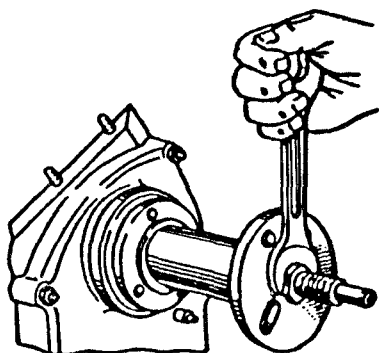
Напрессовка ступицы шкива коленчатого вала с помощью приспособления 16-У-236817
